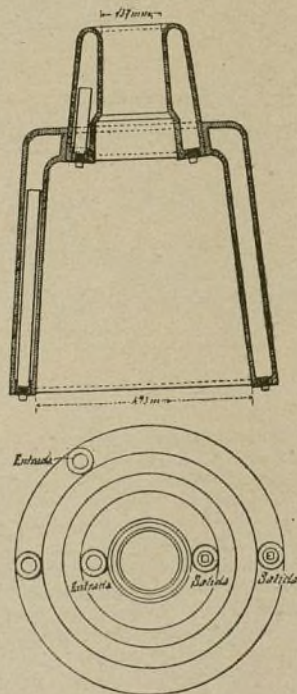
Refrigerador de cobre con la tobera de cobre colocada.
